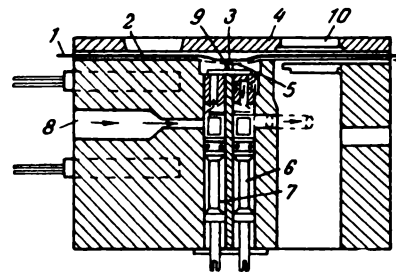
Схема фотопроекторного прибора для покадровой обработки 35-мм тонкослойной пленки [2,17]
